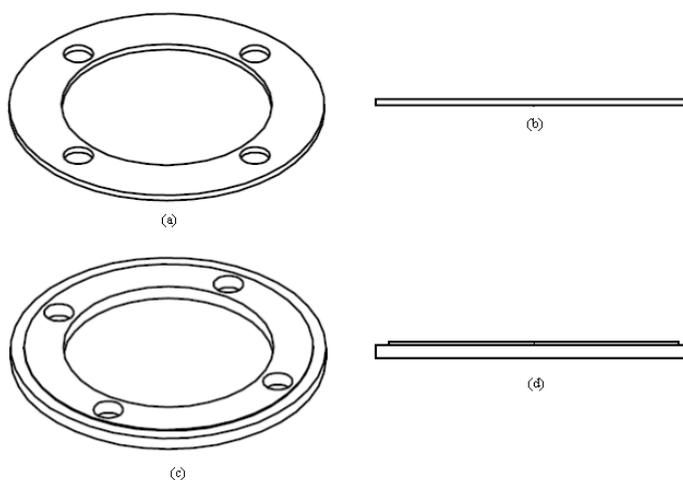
Prospetto (a) dall'alto e (b) laterale della ghiera usata per il fissaggio delle membrane; prospetto (c) dall'alto e (d) laterale della ghiera usata come supporto. Quest'ultima è costituita da uno scanco, visualizzabile nel prospetto laterale, sui sono state disposte le membrane.
